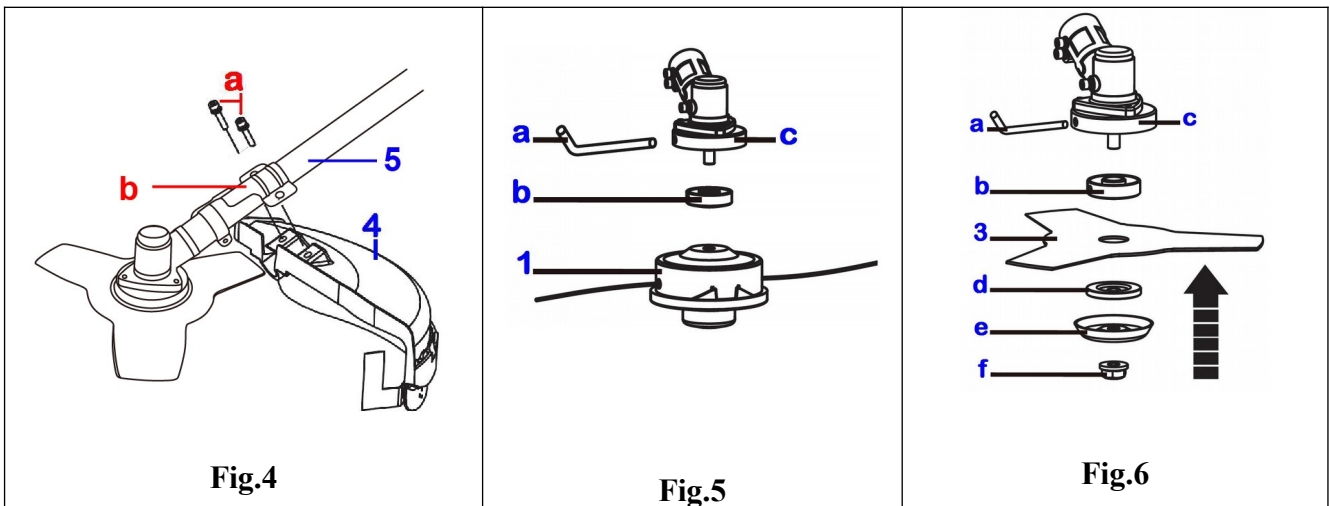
a- Clé ; b- Bague ; c- Carter d'engrenage ; 1- Bobine Fil Nylon
